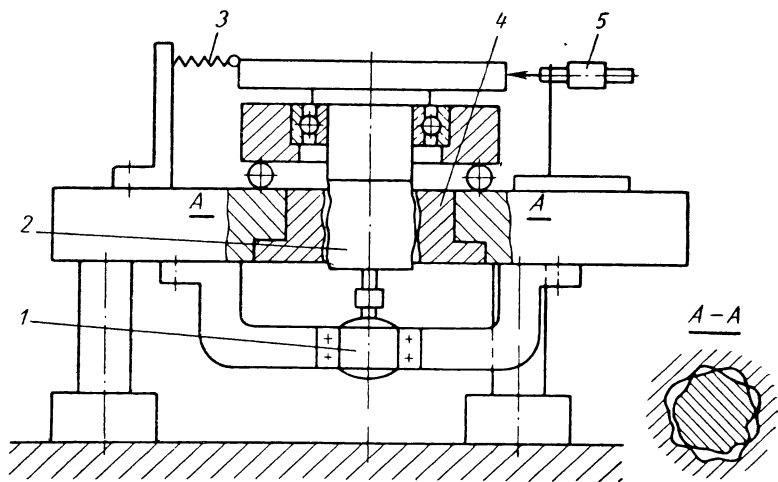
Схема устройства, осуществляющего сложное движение измеряемой детали
